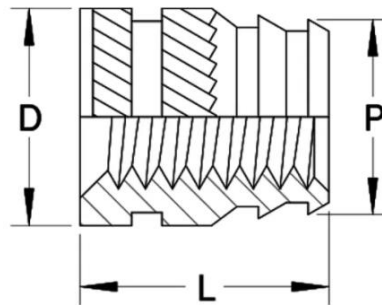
Imagen demostrativa sobre dimensiones del inserto.
